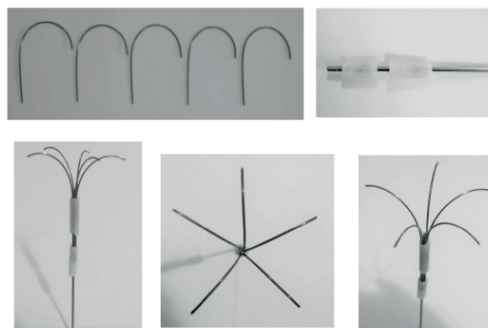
Hastes memorizadas e eletrodo 5H montado para a soldagem com dispositivo impresso em impressora 3D.
